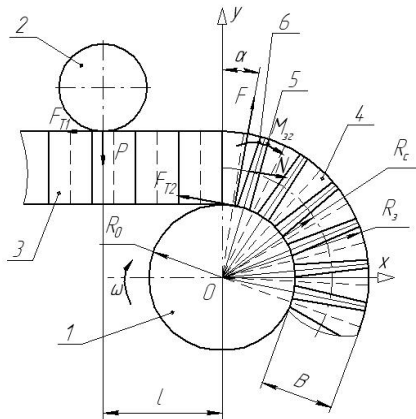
Схема дії сил у процесі навивання гофрованої стрічки на оправку: 1-оправка; 2-притискний ролик; 3-гофрована стрічка; 4-гвинтова гофрована заготовка. 5, 6-лінії згину
